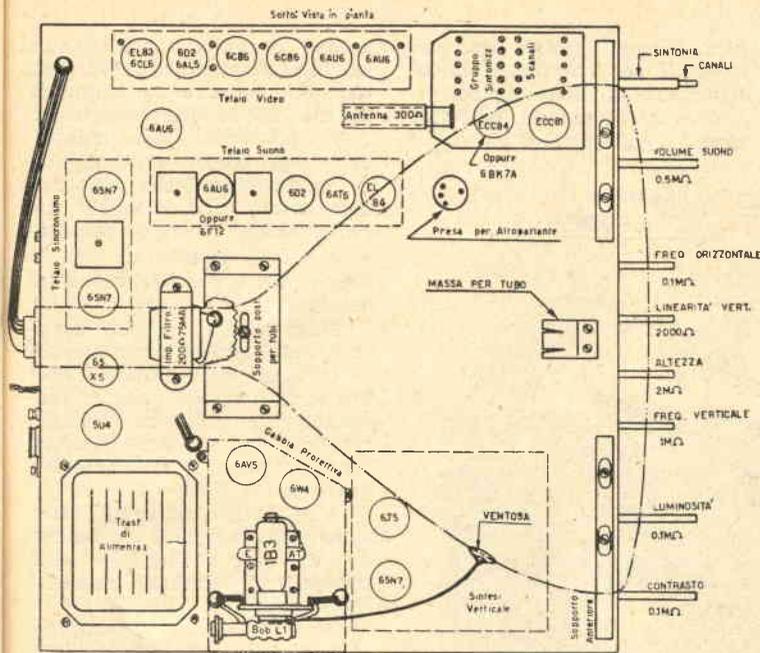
Vista dall'alto della disposizione dei componenti il televisore.
